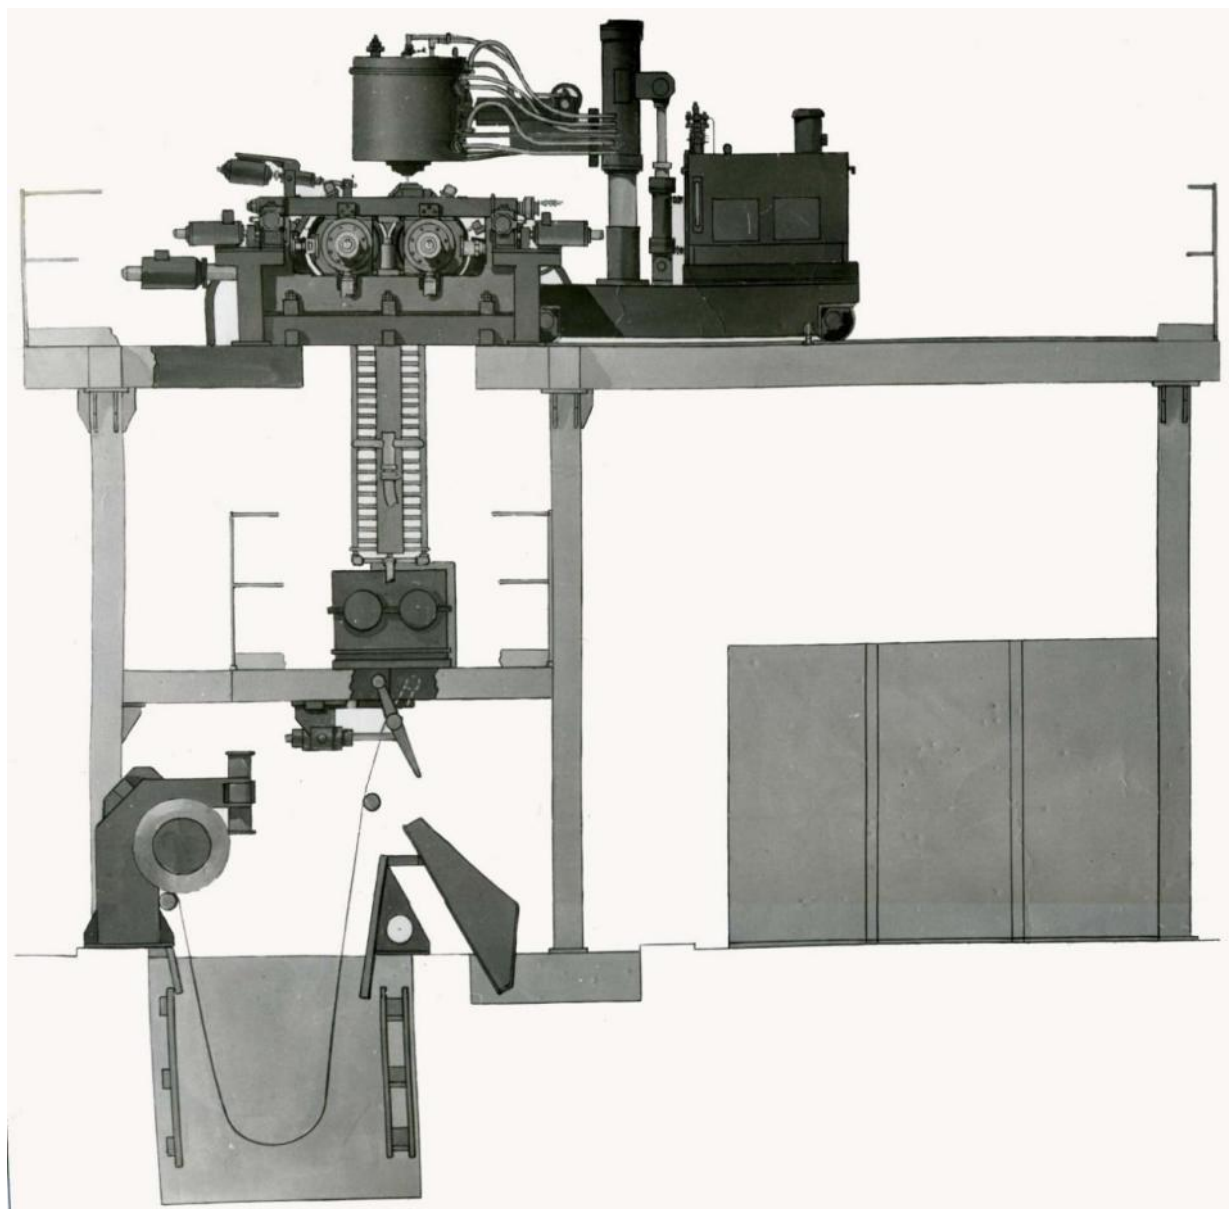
Валковый литейно-прокатный агрегат АМКЛ-300
